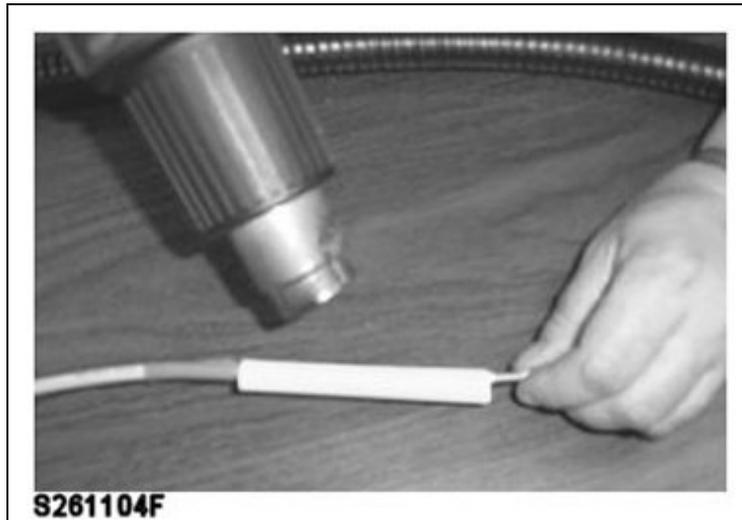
Mise en place du tube thermorétractable sur la connexion
